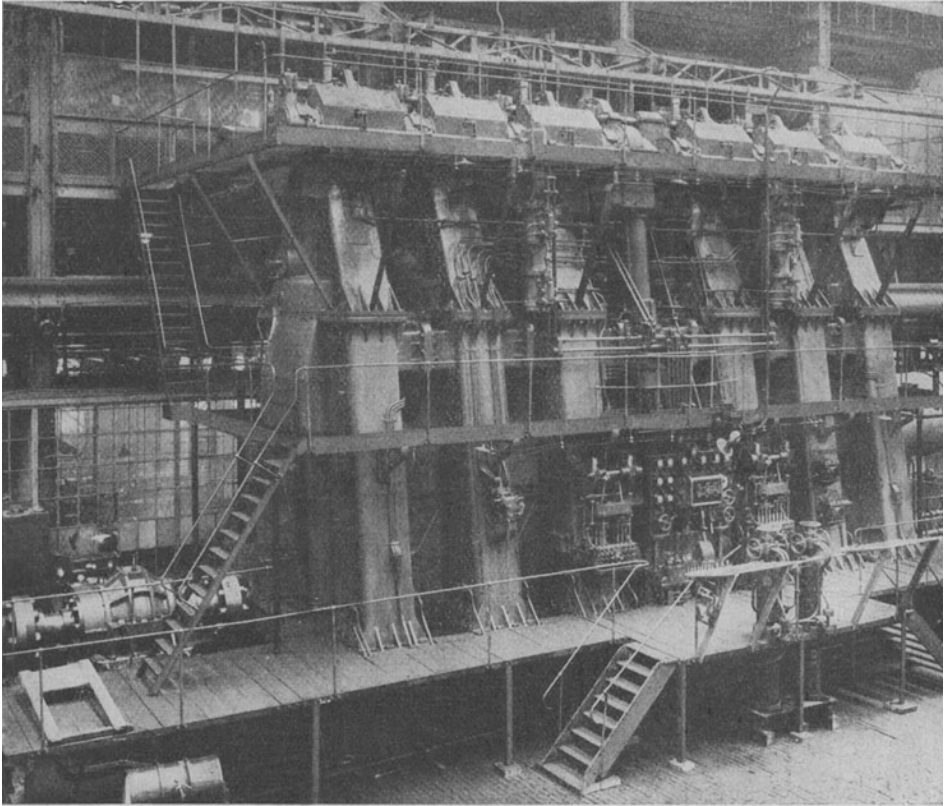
MAN-Viertaktölmaschine, 1800 PS.
